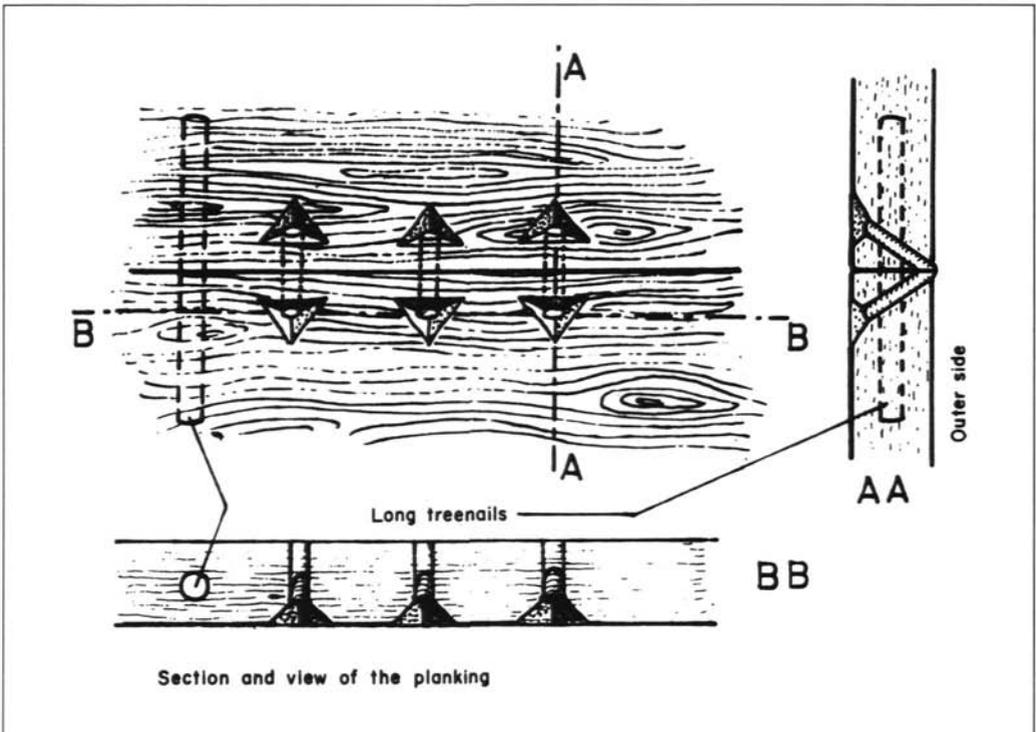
Sistema de ensamblaje utilizado en la nave de Bon Porté. (J. P. Joncheray)
